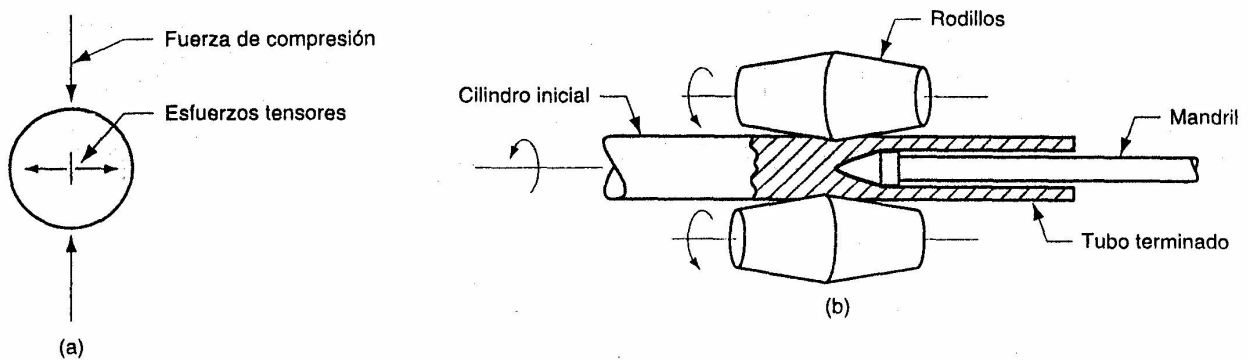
Perforación de rodillos: (a) formación de esfuerzos internos y de la cavidad por compresión de la parte cilíndrica y (b) disposición del molino de laminación Mannesmann para producir tubo sin costura.
